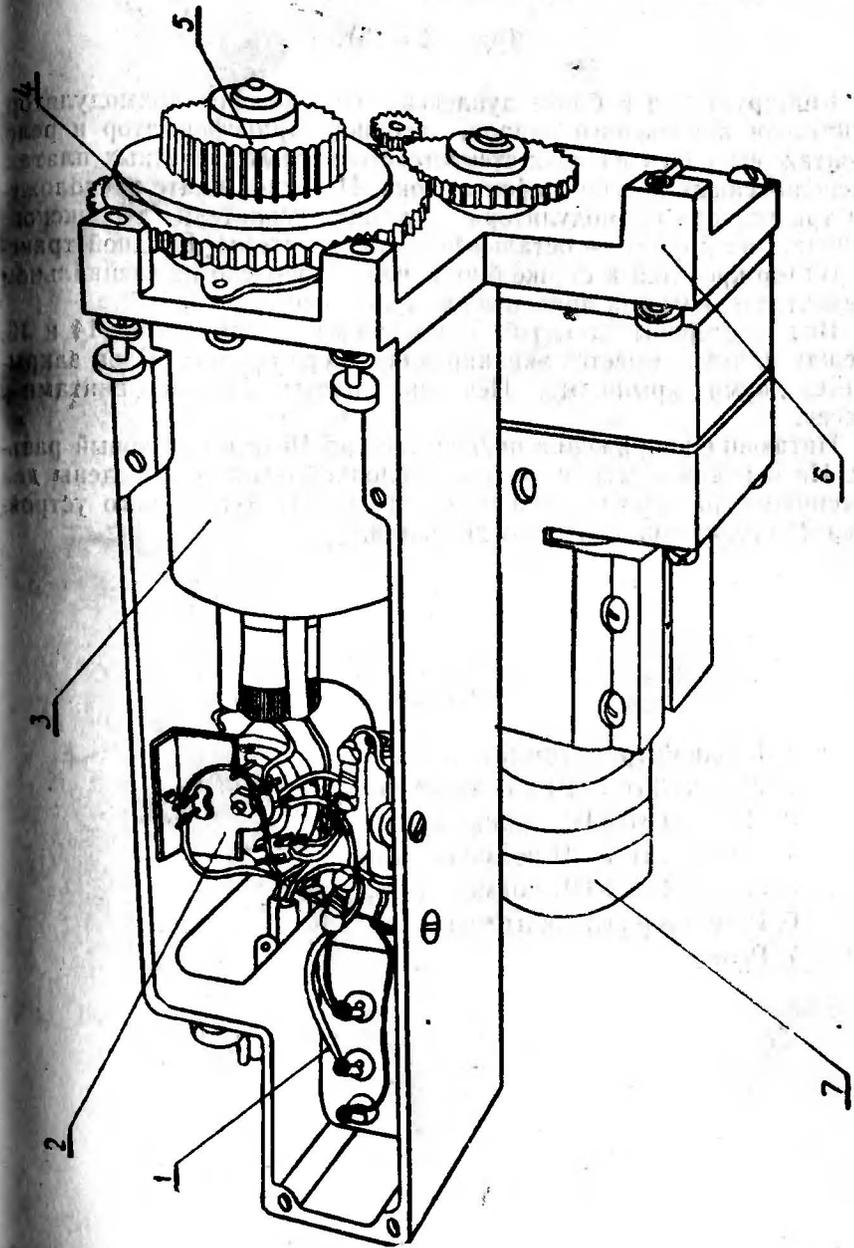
Расположение деталей и монтажа блока мотора — блока № 6
